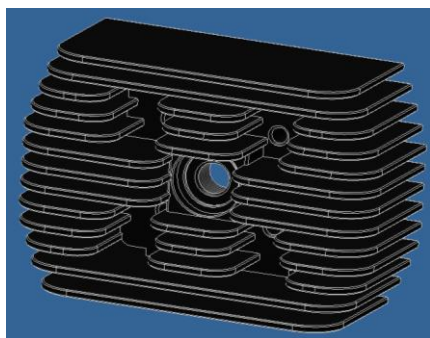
Detail zešikmeného otvoru pro zapalovací svíčku
